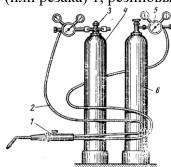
Сварочный пост для газовой сварки и резки:1 — горелка; 2 — шланг; 3— вентиль; 4— кислородный баллон; 5 — ацетиленовый редуктор; 6 — баллон с ацетиленом
